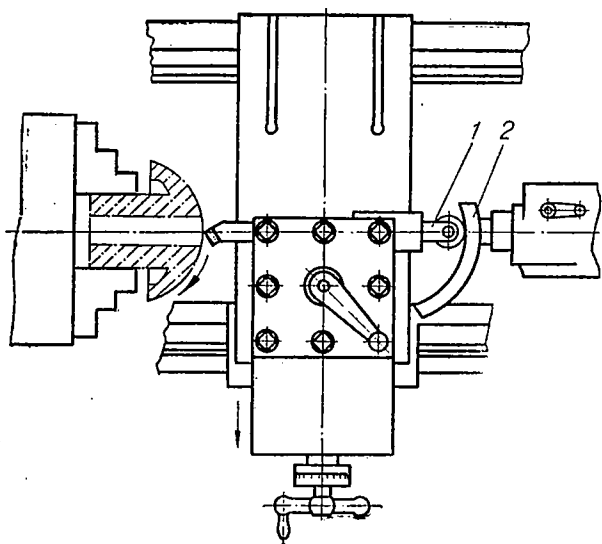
Приспособление к задней бабке токарного станка для обработки фасонных поверхностей.
